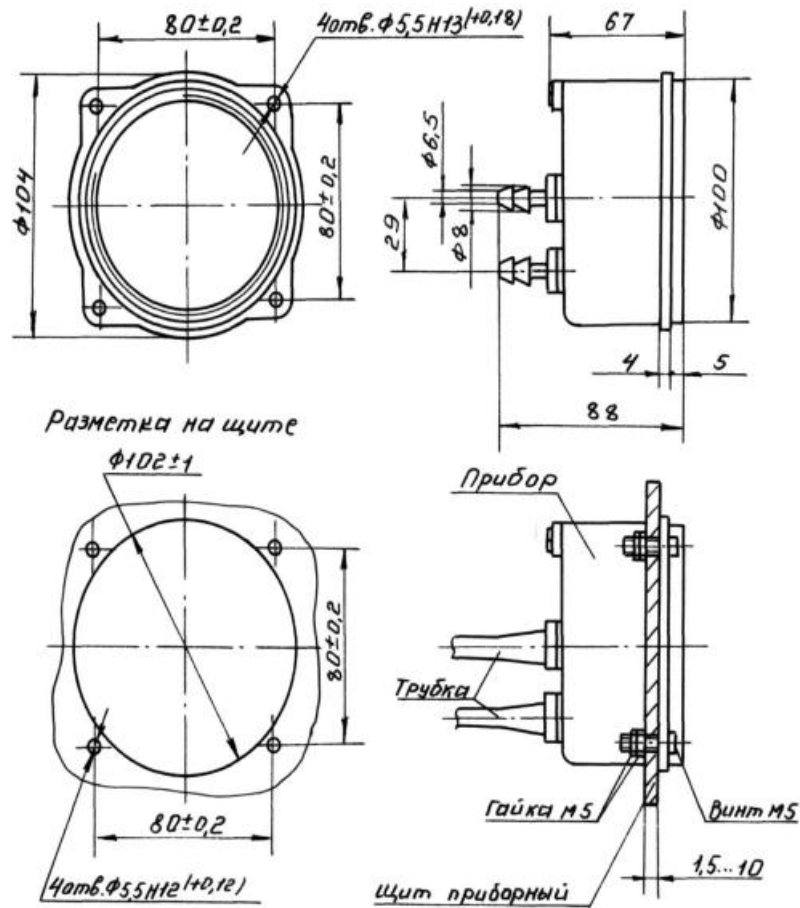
Габаритные и присоединительные размеры приборов (для исполнения «Астр»)
